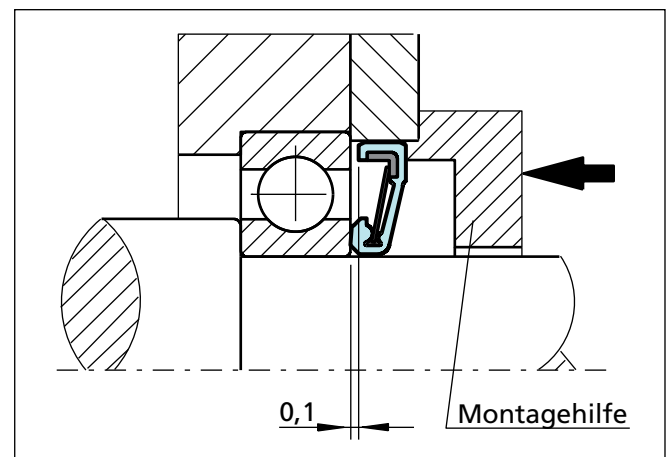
Einbau der Axial-Wellendichtung mit Montagehilfe
